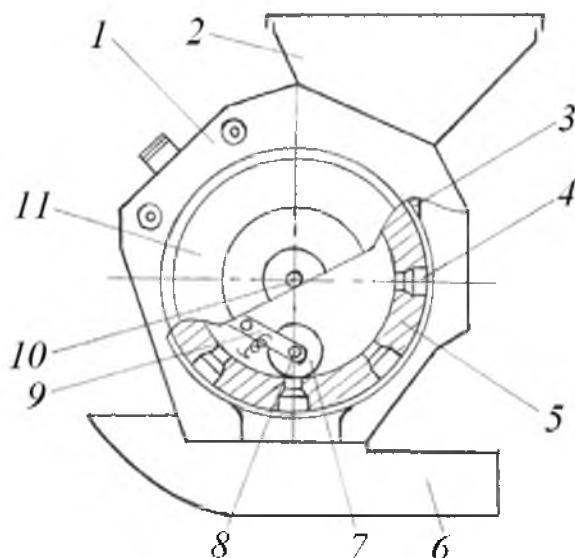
Висівний апарат: 1 – корпус; 2 – бункер; 3 – камера забору; 4 – комірка; 5 – висівний диск; 6 – сошник; 7 – ролик; 8 – вісь; 9 – вилка; 10 – вал; 11 – кришка.
